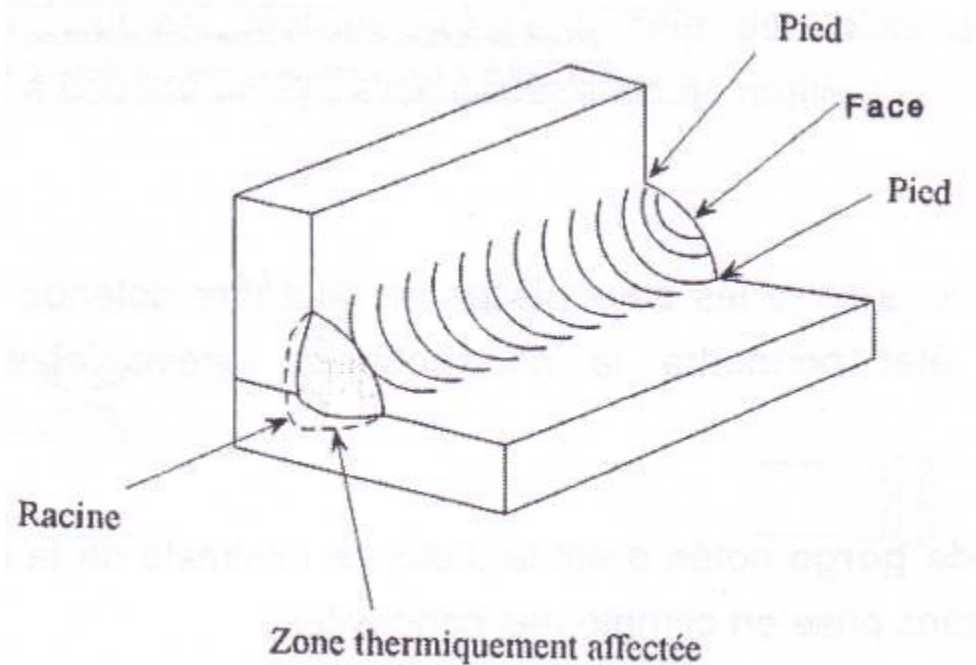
Description d'un cordon de soudure (<http://poste-a-souder.comprendrechoisir.com/comprendre/soudure-aluminium>)
